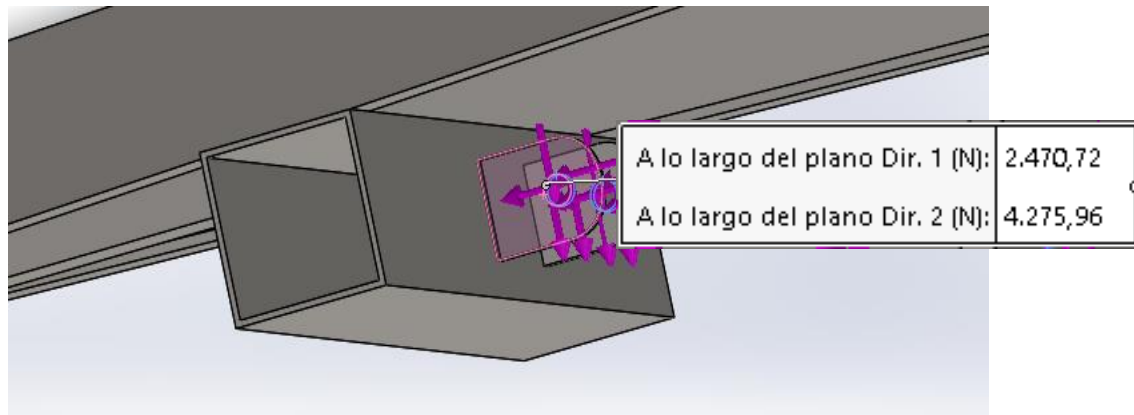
Fuerza del cilindro aplicada sobre las plaquetas del chasis fijo.
